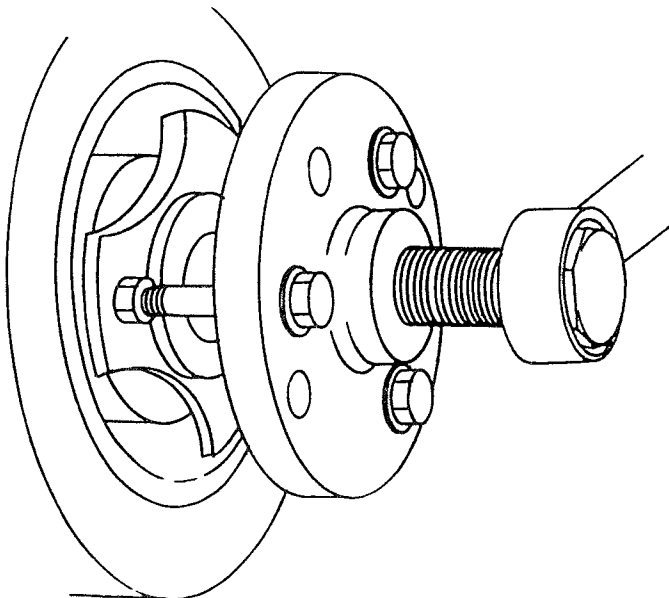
Abziehen des Schwingungsdämpfers. Abziehschrauben in die Bohrungen eindrehen und mit einem Ringschlüssel die Mittelschraube anziehen.
